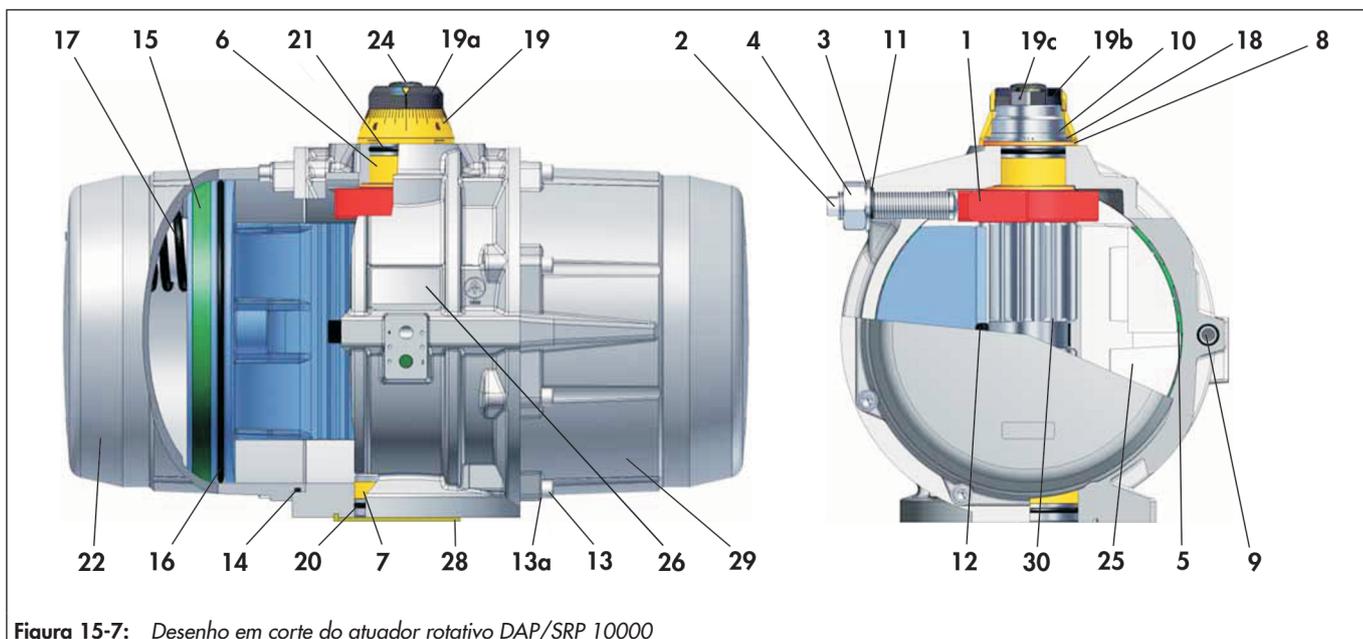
Desenho em corte do atuador rotativo DAP/SRP 10000
